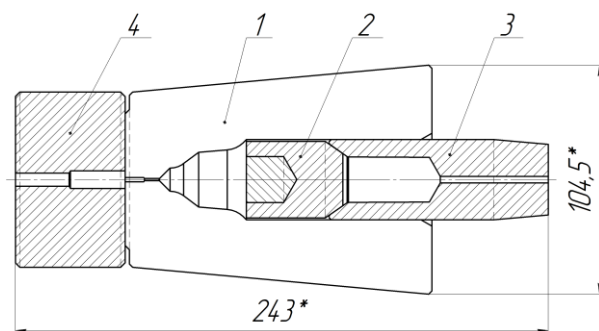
Внешний вид экспериментальной оснастки для изготовления резцов
